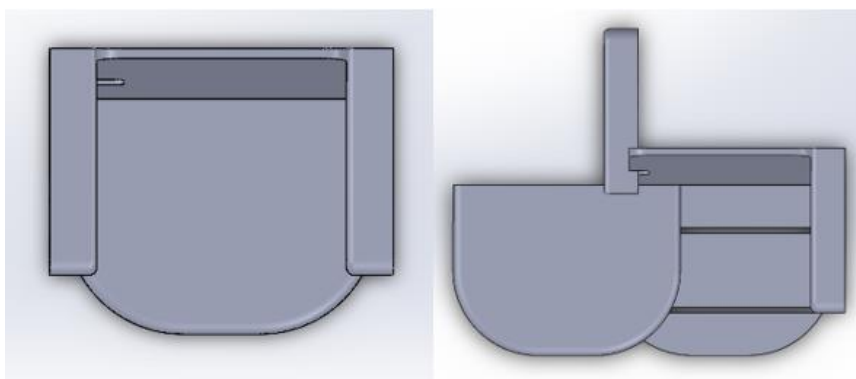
Vista en planta de las dos posiciones para el reposabrazos. Fuente: Propia.
